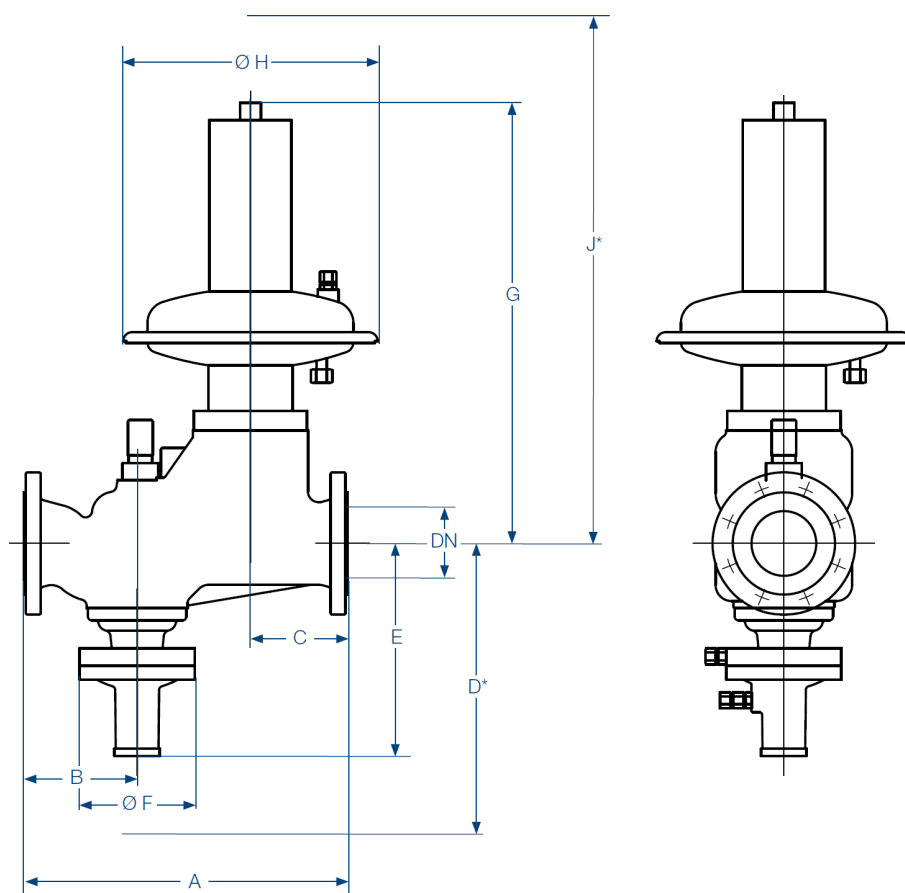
Габаритные размеры регуляторов HON330 (Ду80, Ду100)
